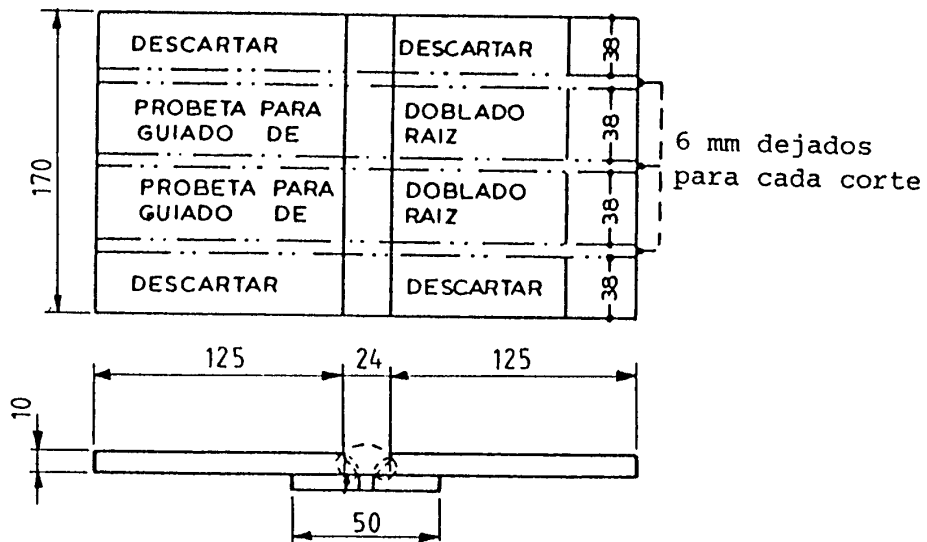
Junta de tope para calificar soldadores de planchas o cañerías de 10 mm de espesor
